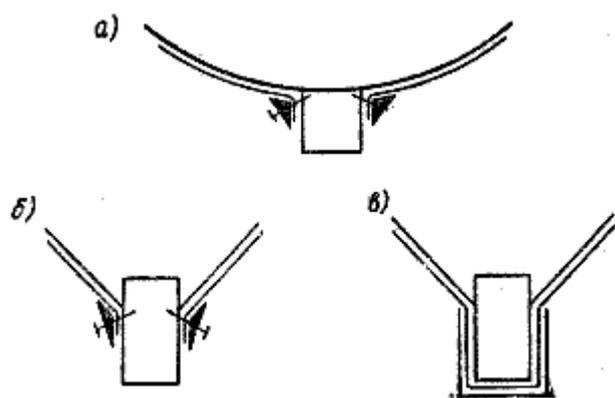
Оклейка корпуса тканью: а — у киля о креплении рейкой на гвоздях; б — штевня с креплением рейкой; в — у штевня — оклейка вокруг.
